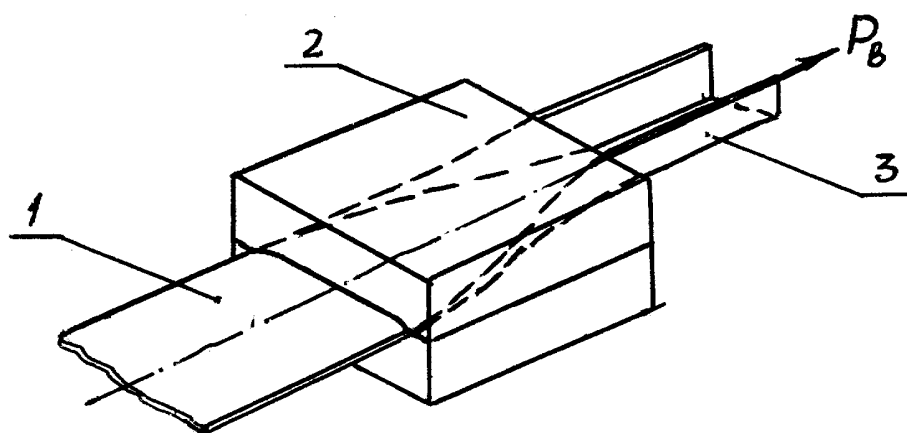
Метод изготовления профилей с использованием инструментальной фильеры: 1 – листовая заготовка; 2 – фильера; 3 – профиль
